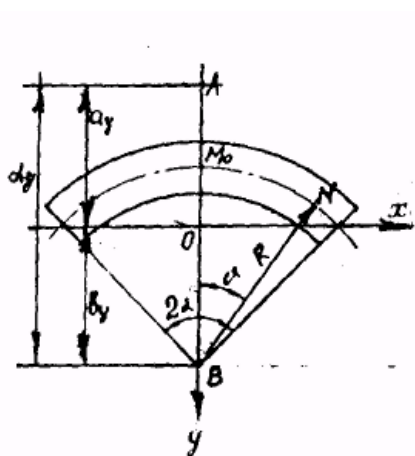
Схема расположения координатных осей по сечению заготовки: R - радиус дуги срединной линии сечения заготовки; S - толщина стенки сечения заготовки; α - половина центрального угла.
